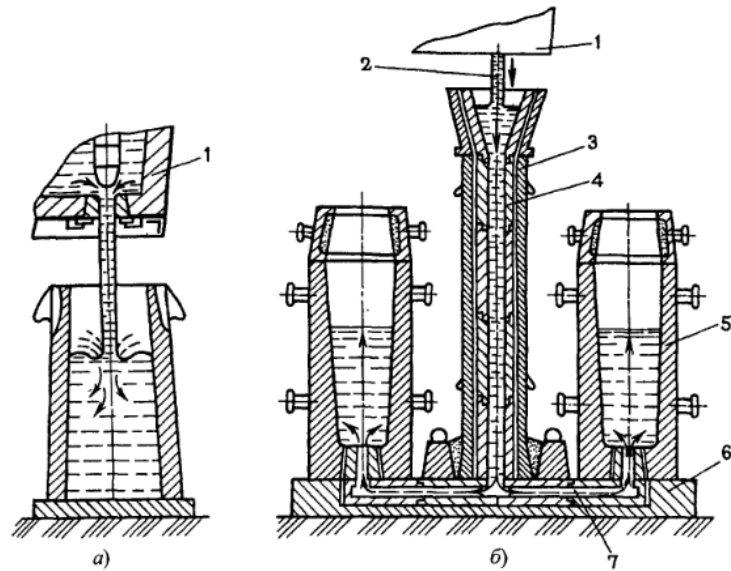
Способы разливки стали в изложницы: а - сверху; б - снизу
